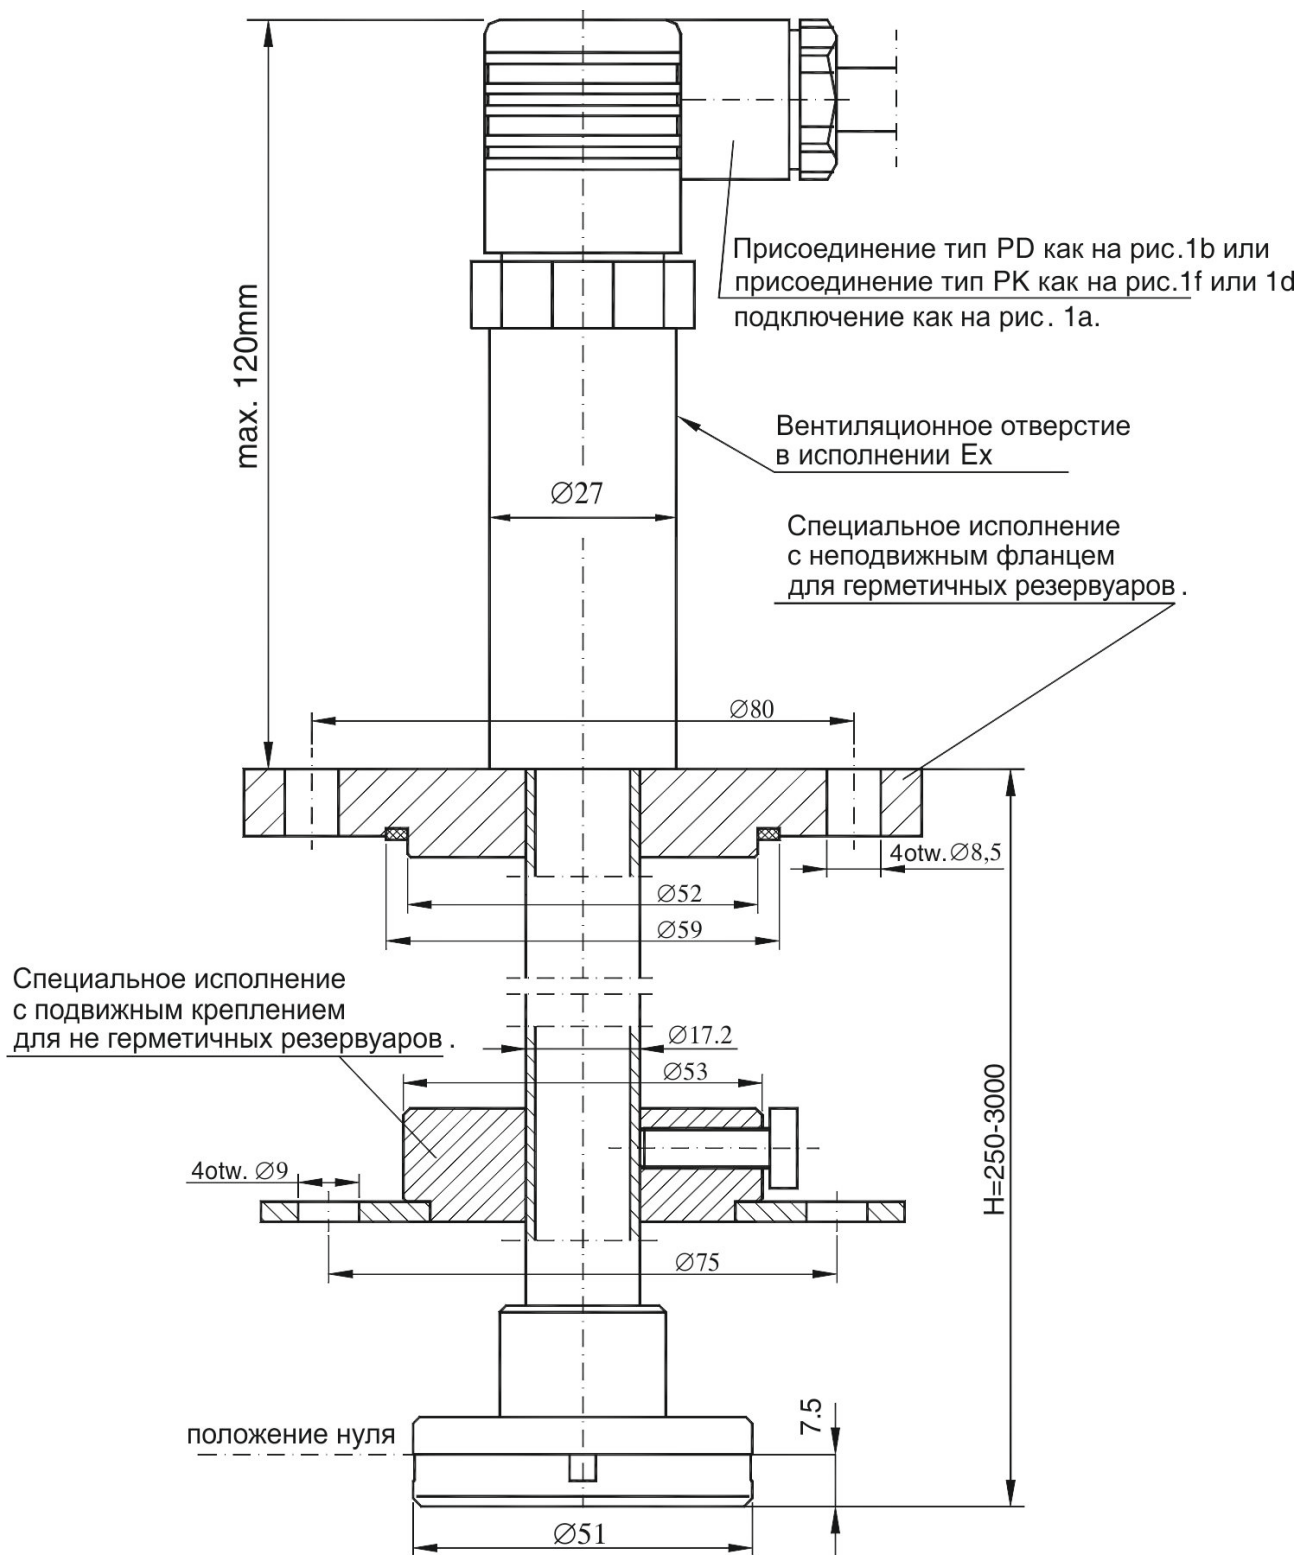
Преобразователь РС-28Р. Габаритные размеры.
